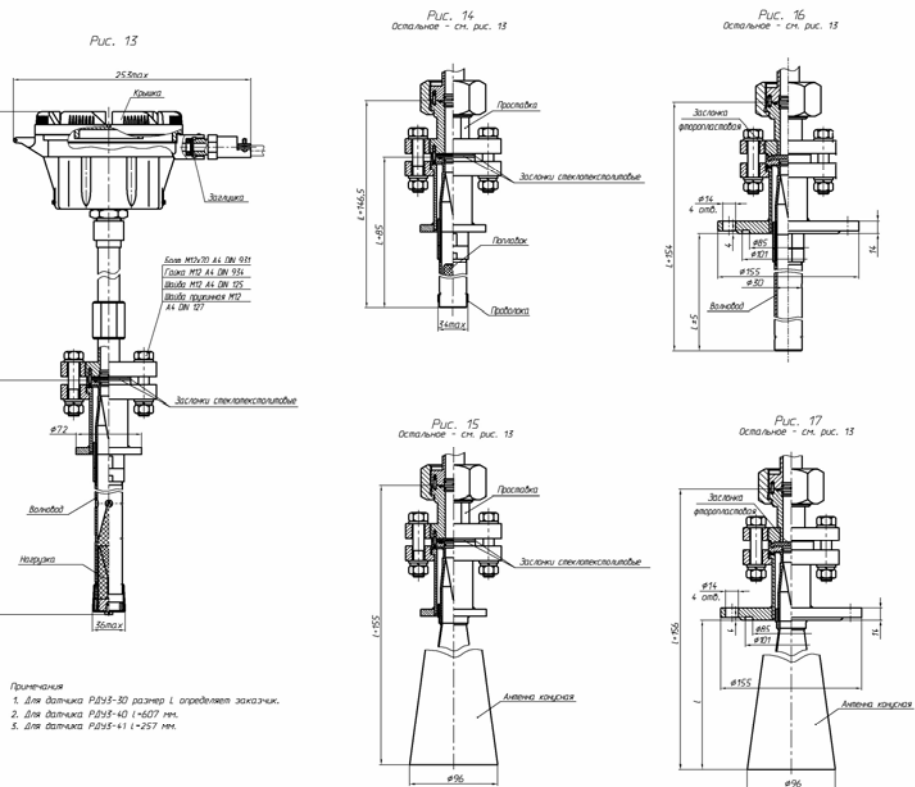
Габаритные и установочные размеры датчиков РДУЗ, часть 3
